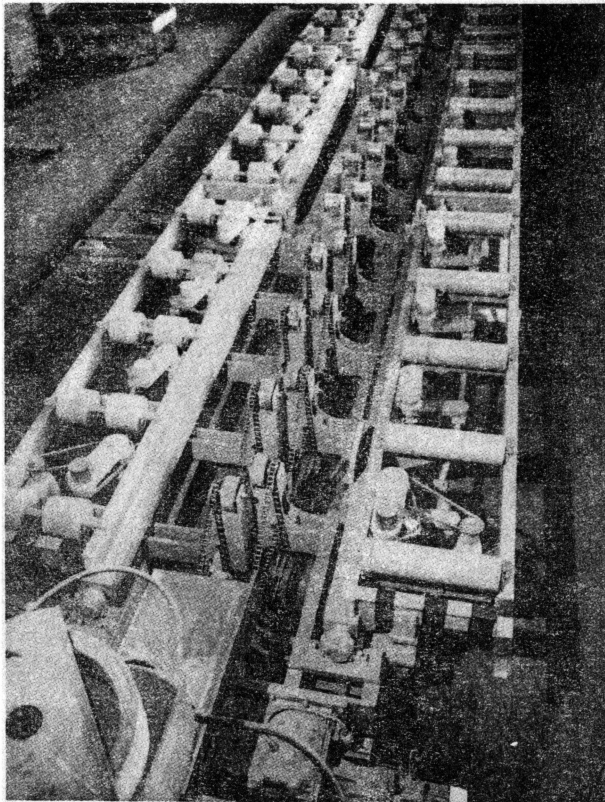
Einlegestation der Blechträgerdurchlaufschweißanlage, die Rollengänge rechts und links sind hochklappbar
